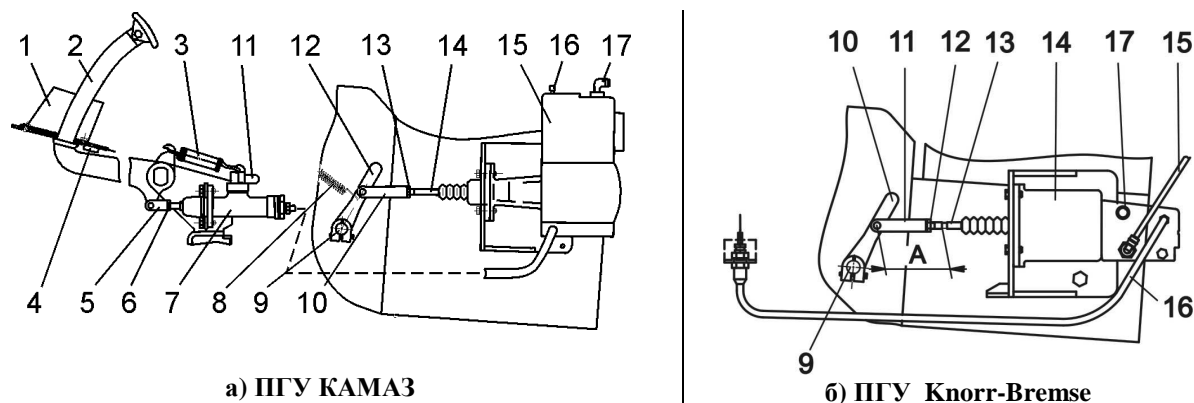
Привод сцепления автобуса ПАЗ-4234
